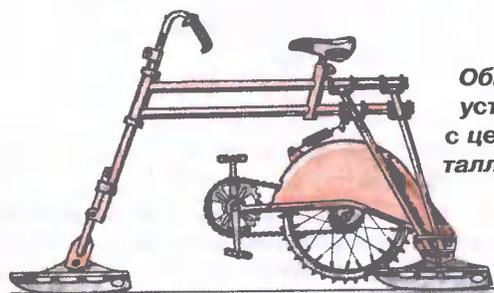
Общий вид устройства с цельнометаллической рамой.
